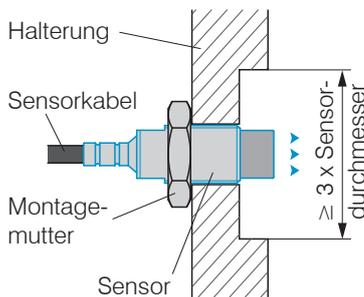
Flächenbündige Montage eines ungeschirmten Sensors in einer metallischen Halterung mit Aussparung
